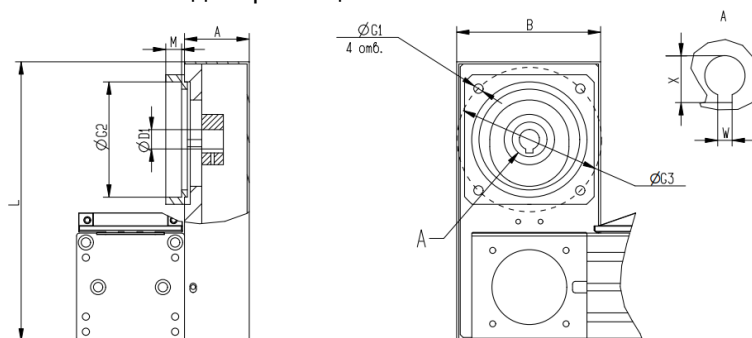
Набор для параллельной установки редуктора PR-MCR-80 с фланцем.
